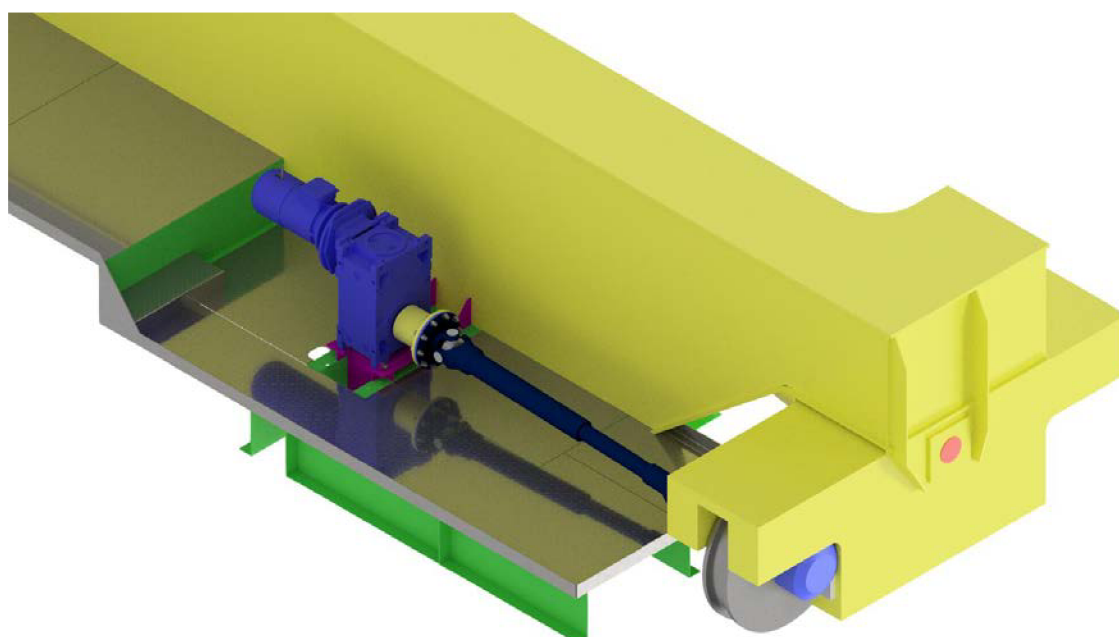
Mechanismy pojezdu – IZO pohled 4
